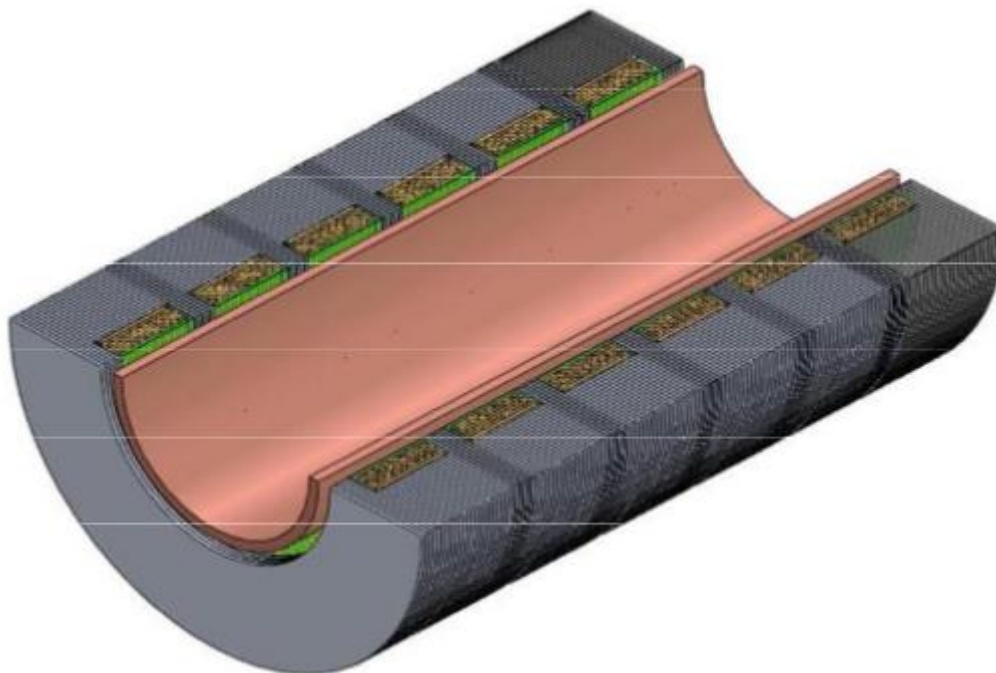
Géométrie et dimension de la machine linéaire a six encoches (coupe 1/2 3D)
